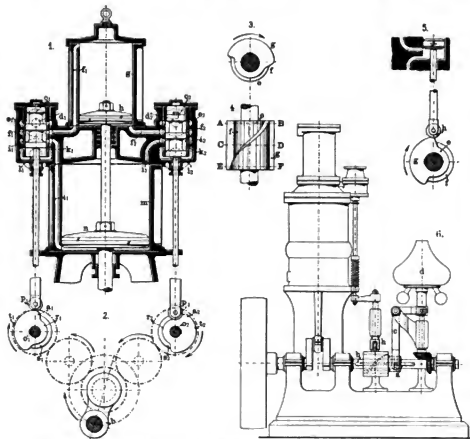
Z. A.: Steuerungsrichtung für Tandemmaschinen.
